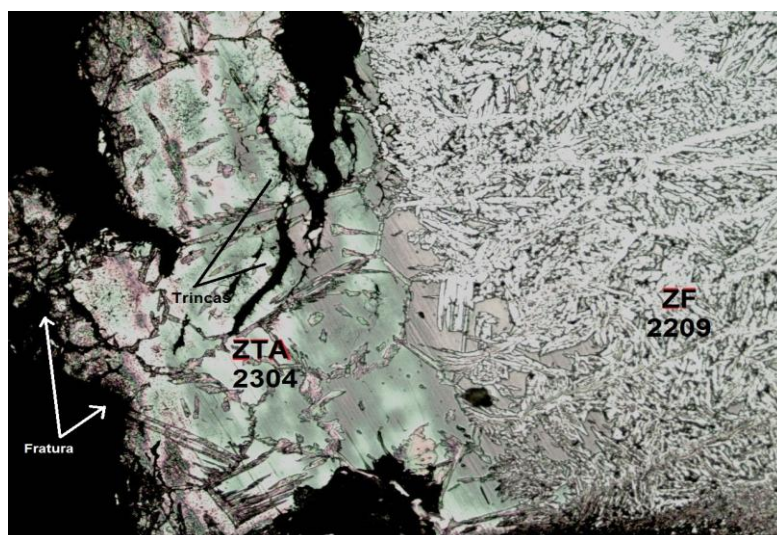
Fratura e trincas transgranulares na ZTA do metal base 2304 após ensaio de CST. Junta soldada com metal de adição 2209
